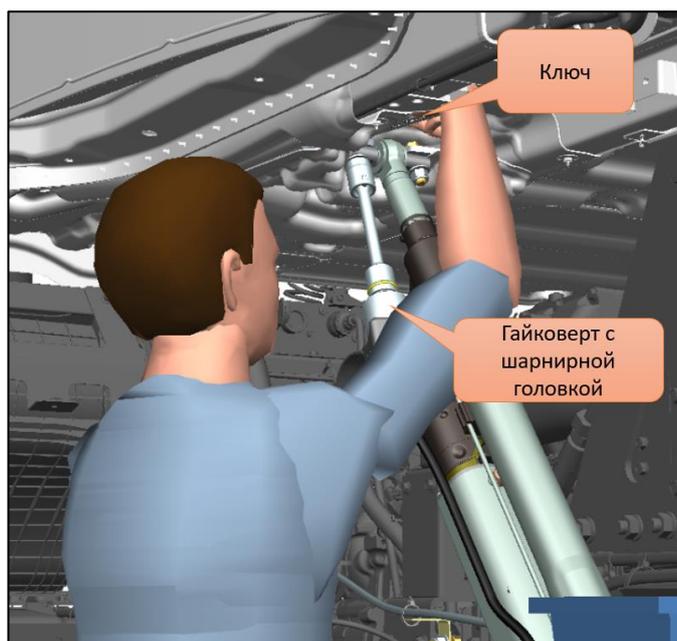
Процесс затяжки гидроцилиндра ключом и гайковертом с шарнирной головкой
